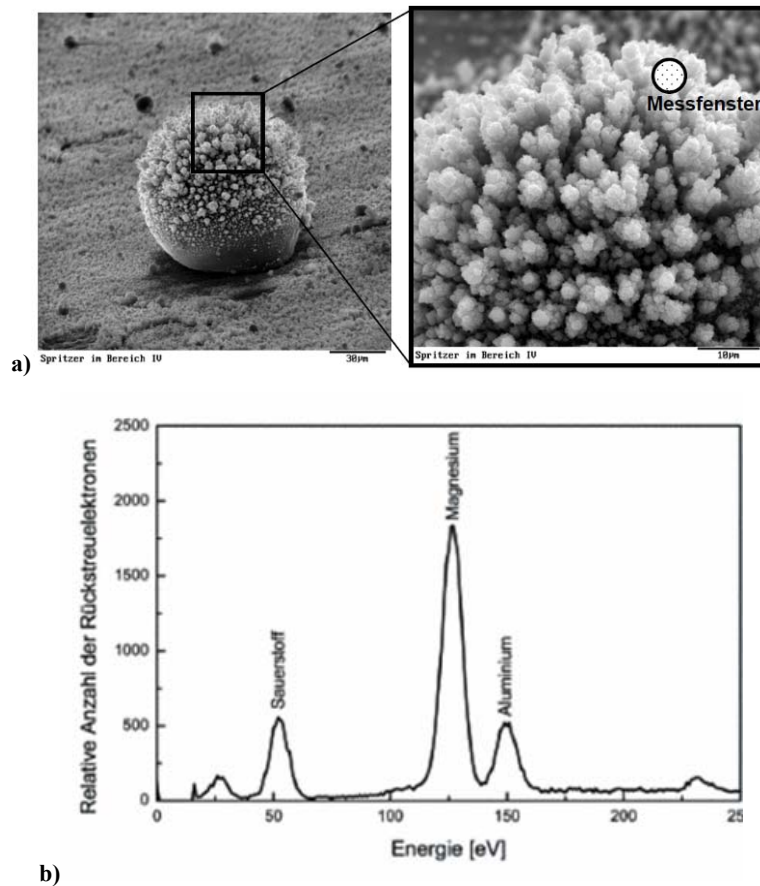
Metalloxidniederschlag auf einem Schweißspritzers von 5182 mit AlMg5 verschweißt a) REM Aufnahme, b) EDX Analyse [Goecke S.F. 2004 S. 78f]
